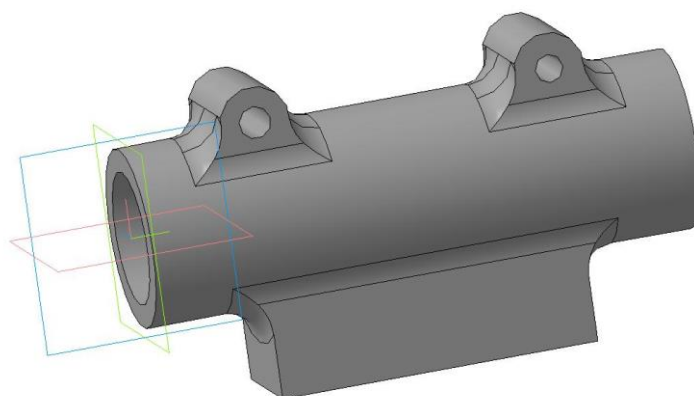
3D модель корпуса БВКС.04.006.090.01
